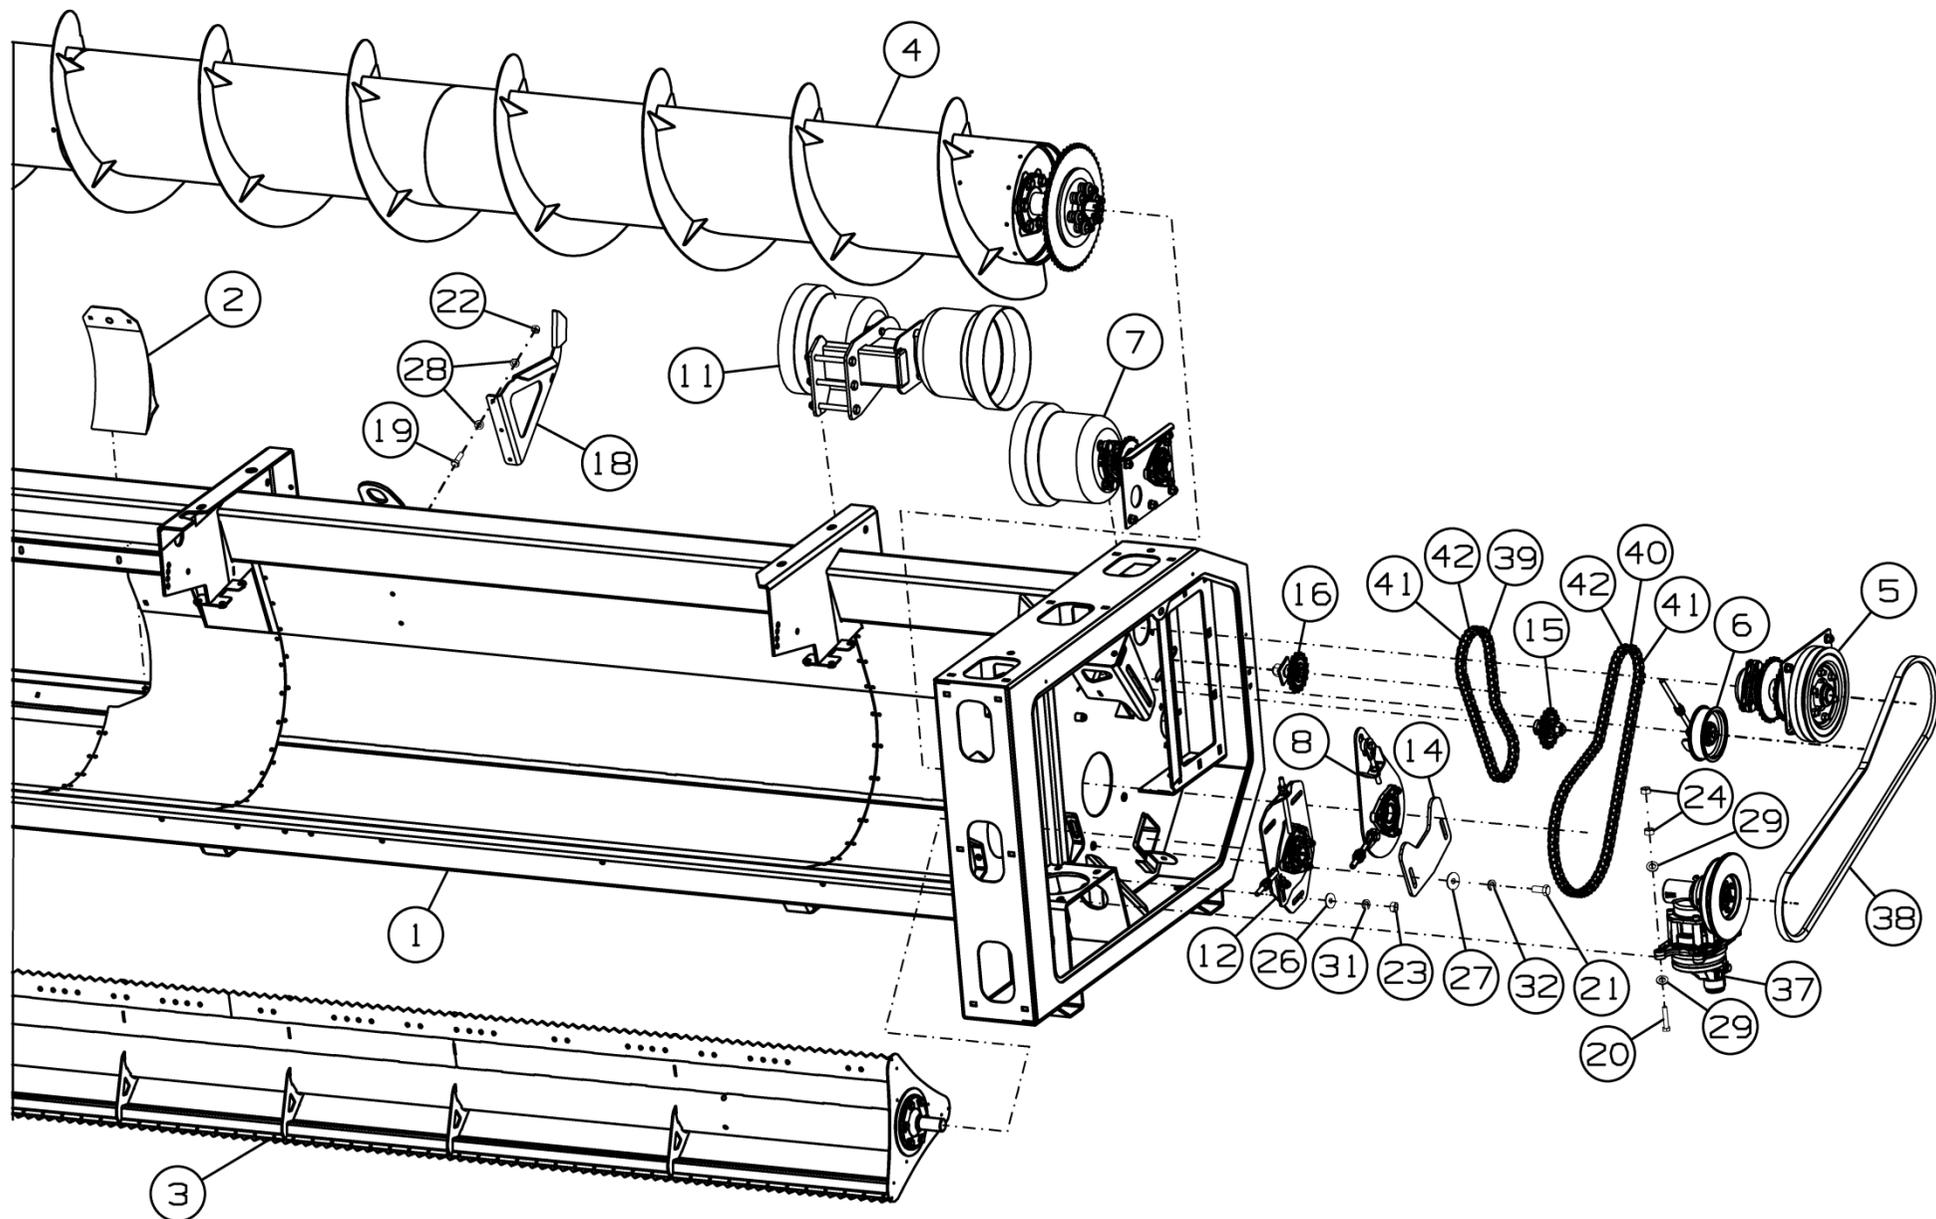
Корпус жатки SS-780.01.01.000У-04
